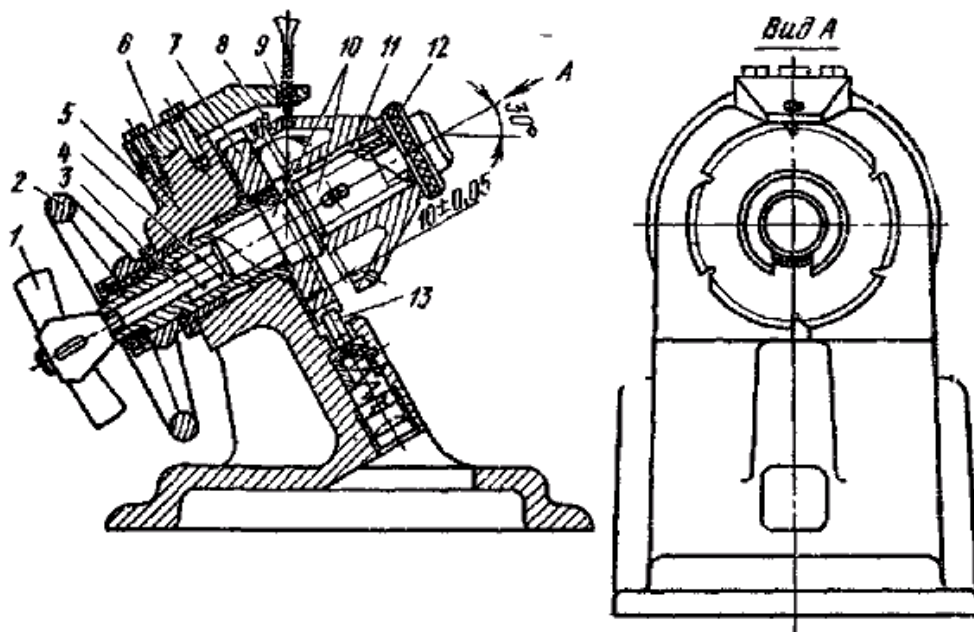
Приспособление с делительным устройством для сверления шести отверстий.
